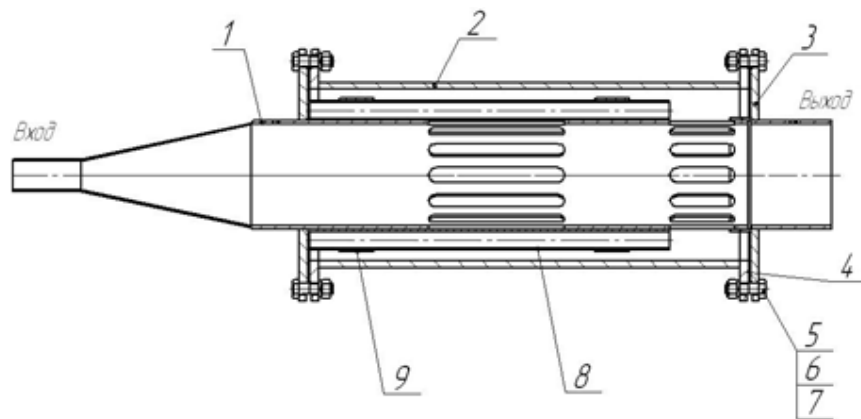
Глушитель шума выпуска винтового компрессора: 1 – внутренний контур; 2 – корпус; 3 – крышка; 4 – прокладка; 5, 6, 7 – болт, гайка, шайба; 8 – трубка-резонатор; 9 – хомут
